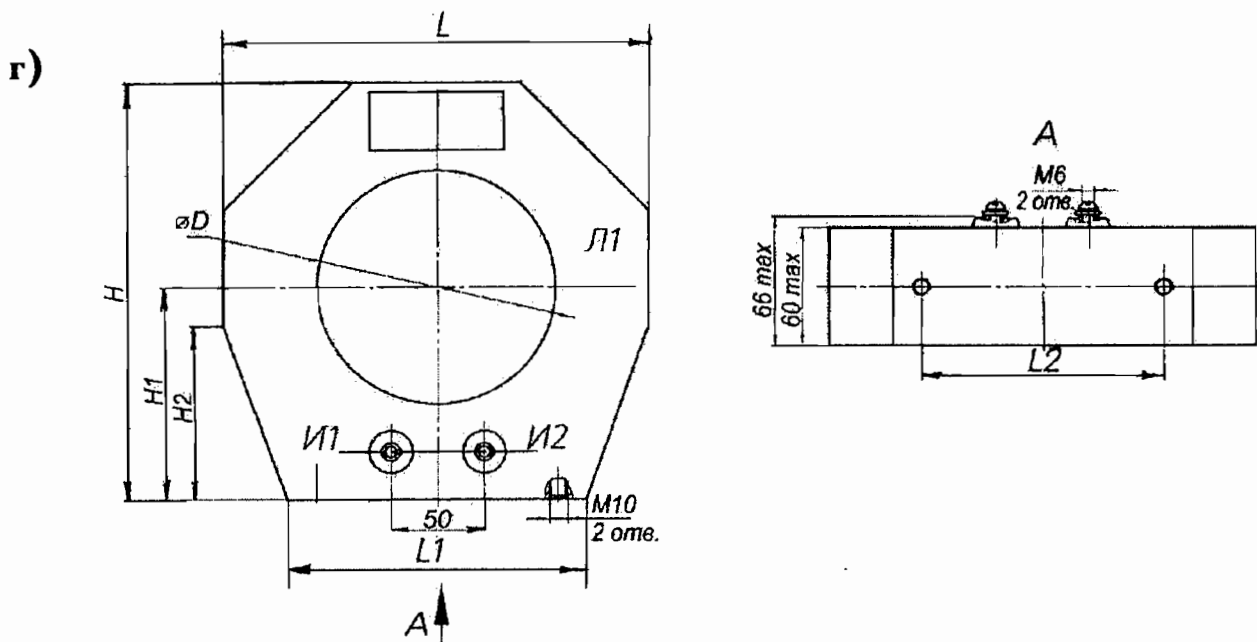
Общий вид и габаритные размеры трансформаторов тока типа ТЗЛК
